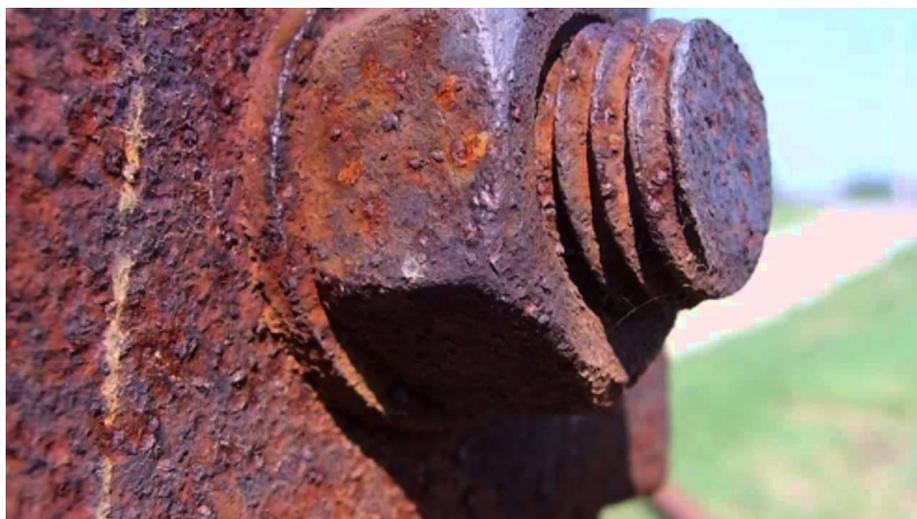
Коррозионный износ болтового соединения комбинированного почвообрабатывающего агрегата
